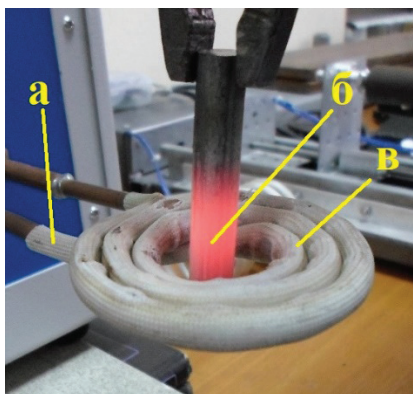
Предварительный нагрев титанового образца перед пластической деформацией: а — изоляция индуктора; б — прогретая заготовка
